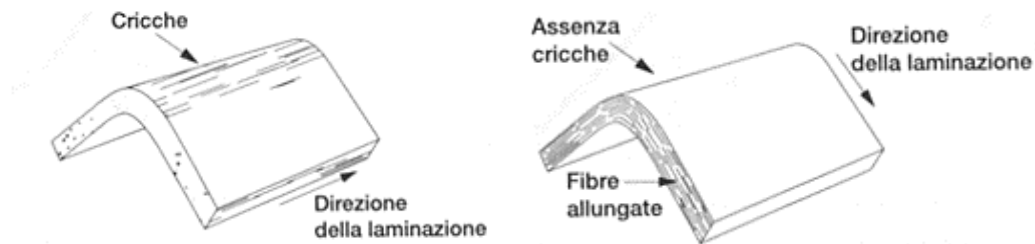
effetto dell'orientamento della direzione di laminazione sulla piegatura [52]
